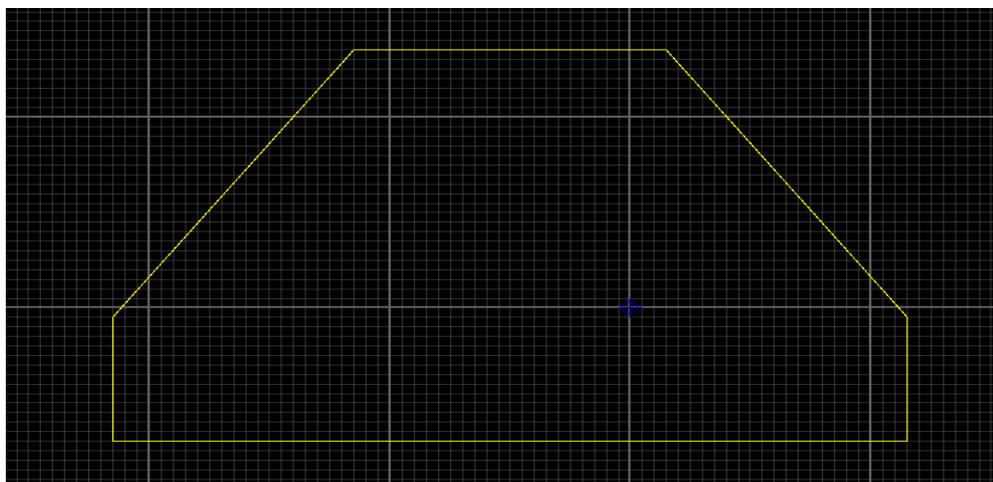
Dimensionar el tamaño que se utilizara para la fabricación del circuito electrónico.
